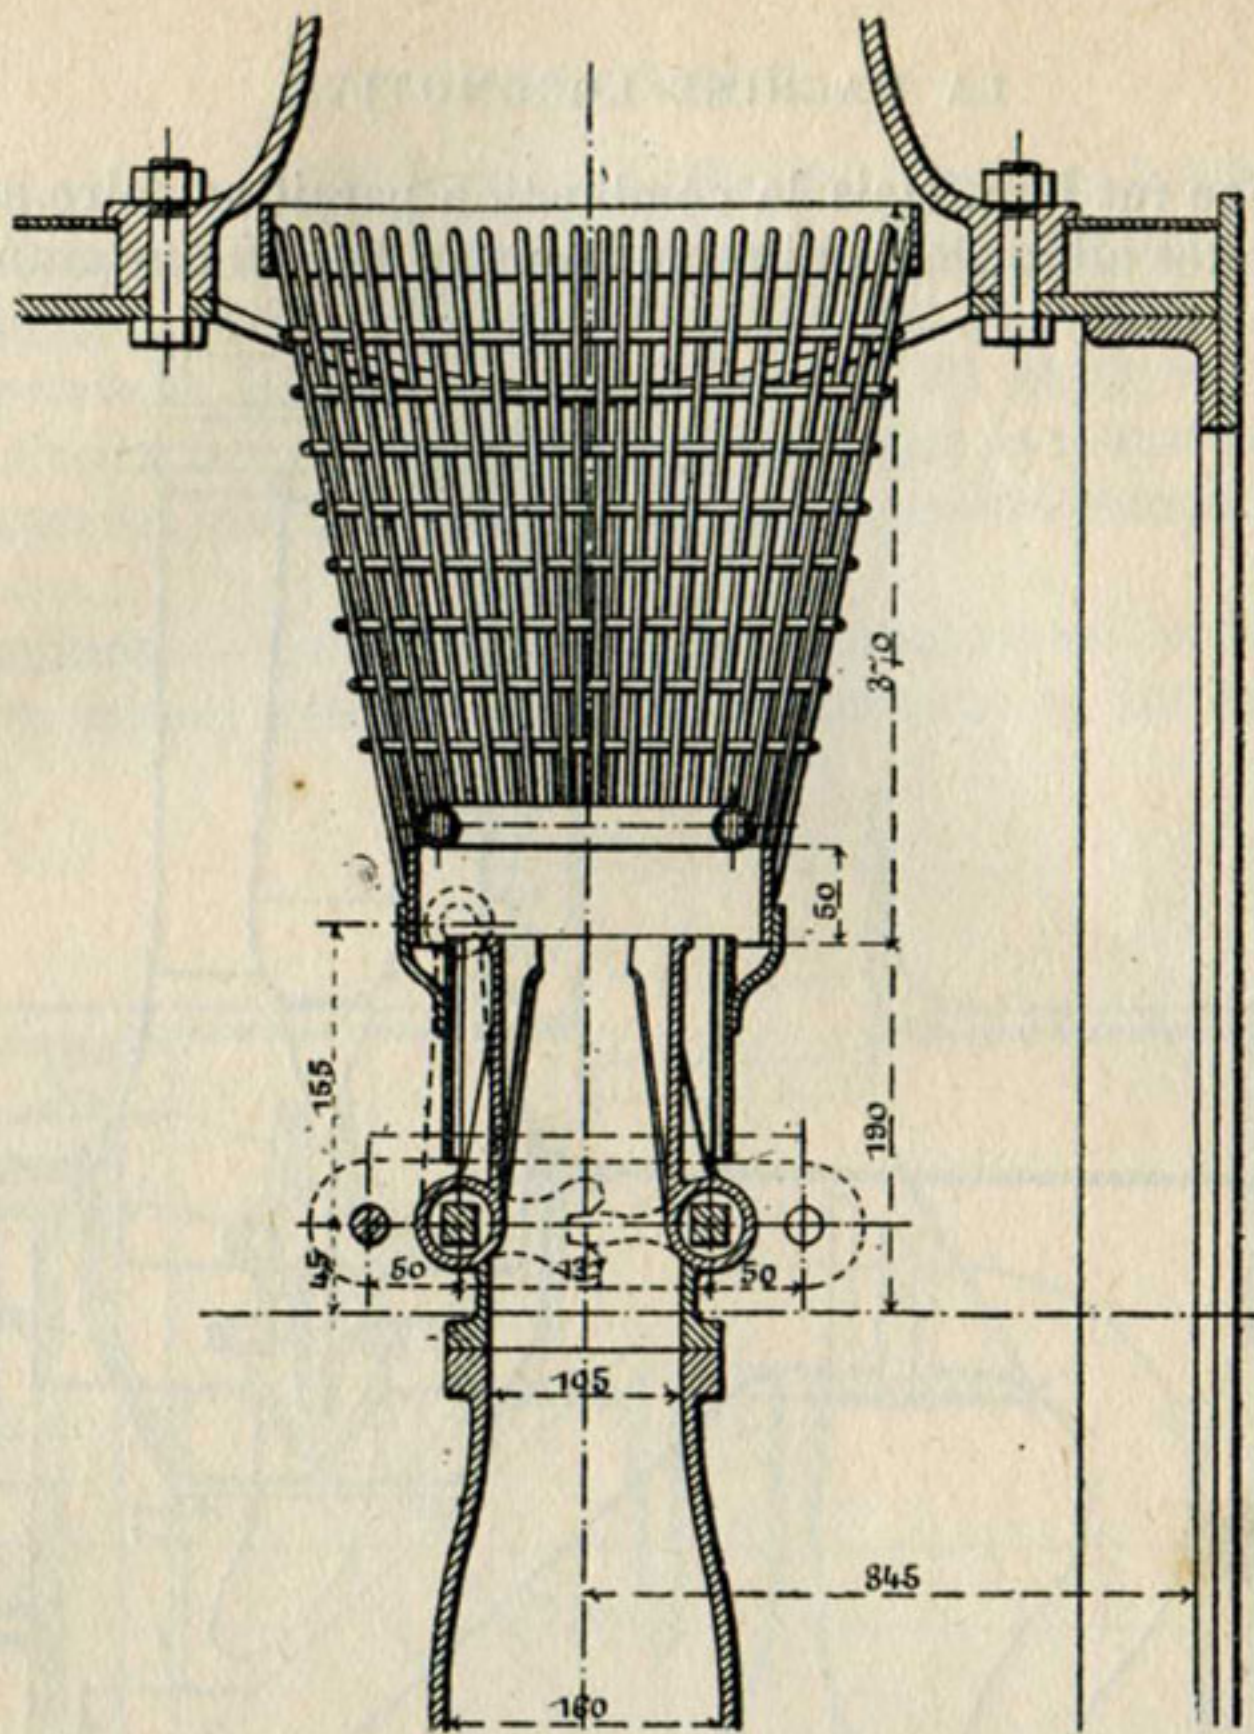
Grille à flammèches des chemins de fer Roumains.
